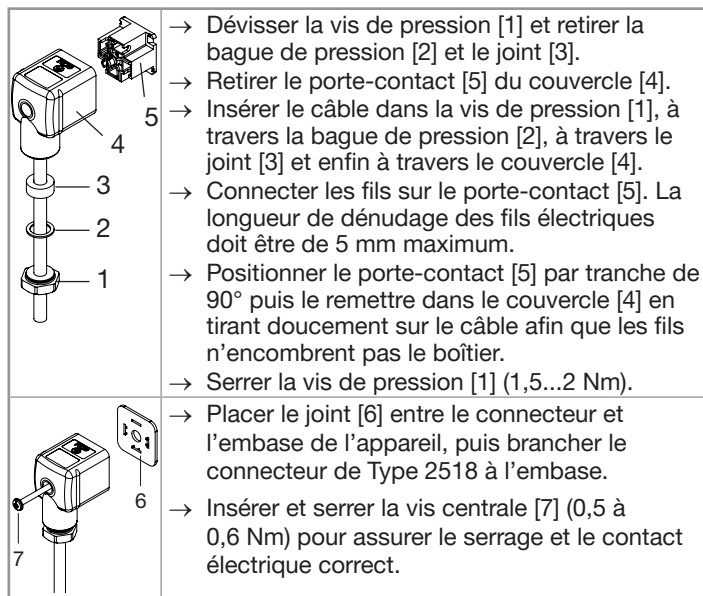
Assemblage du connecteur femelle type 2518 (fourni)
